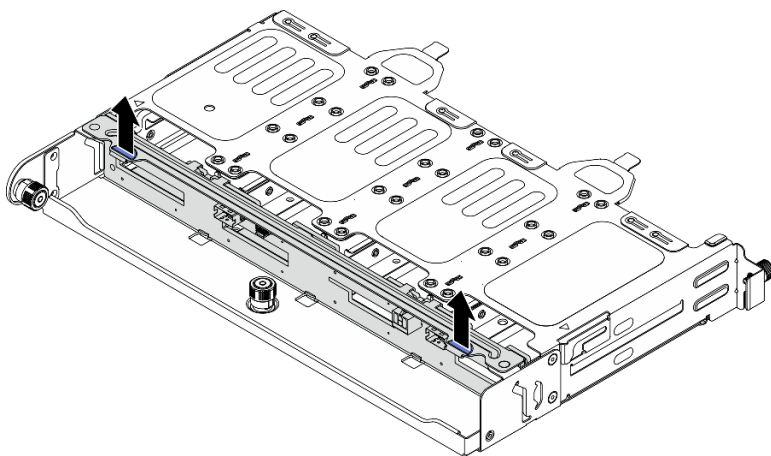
Entfernen der hinteren Rückwandplatine für 8 x 2,5-Zoll-Laufwerke
